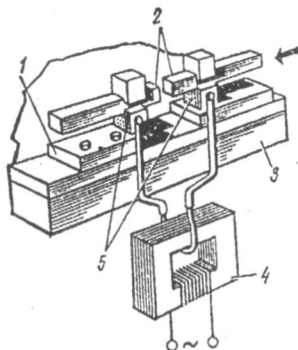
Схема контактной стыковой сварки: 1 - контактная плита; 2 - свариваемые заготовки; 3 - станина; 4 - трансформатор; 5 - электроды
